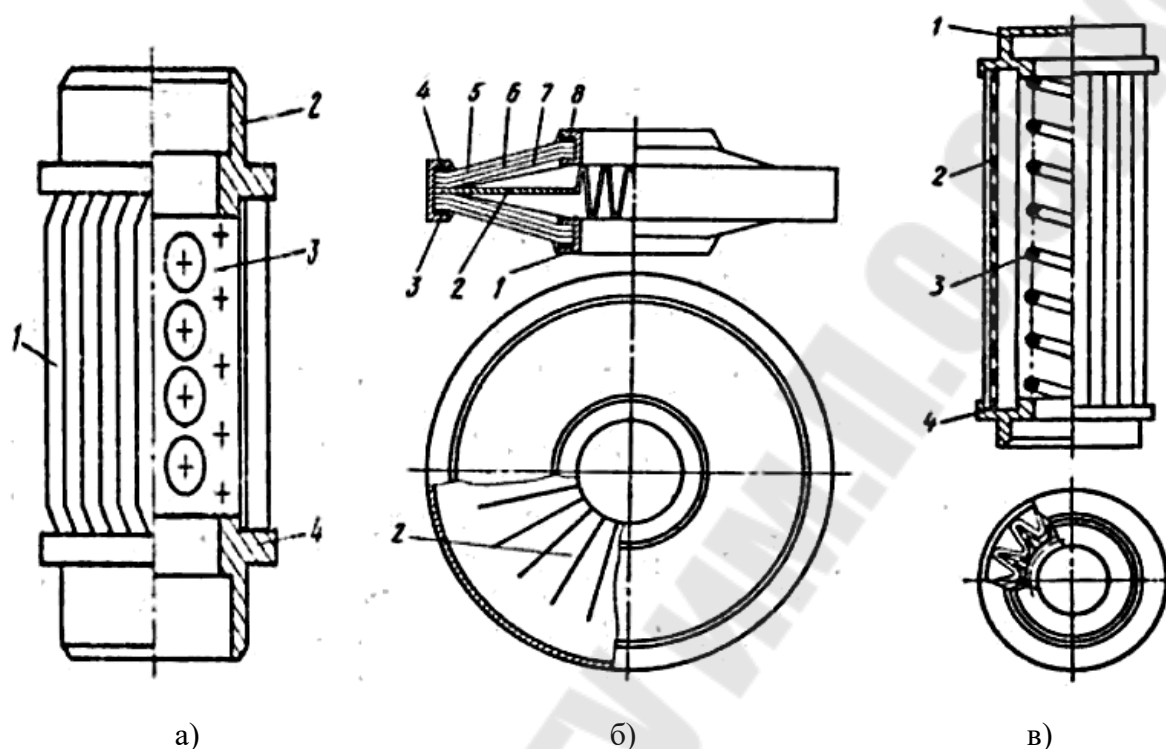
Примеры конструкции фильтроэлементов: а) цилиндрический сетчатый; б) дисковый сетчатый; в) цилиндрический бумажный
